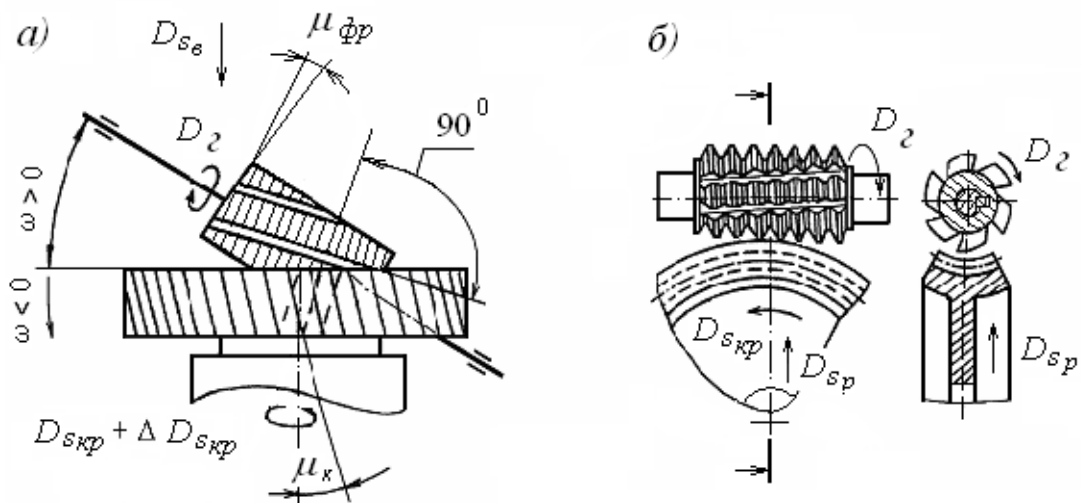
Схемы фрезерования венцов цилиндрического косозубого (а) и червячного (б) зубчатых колёс
